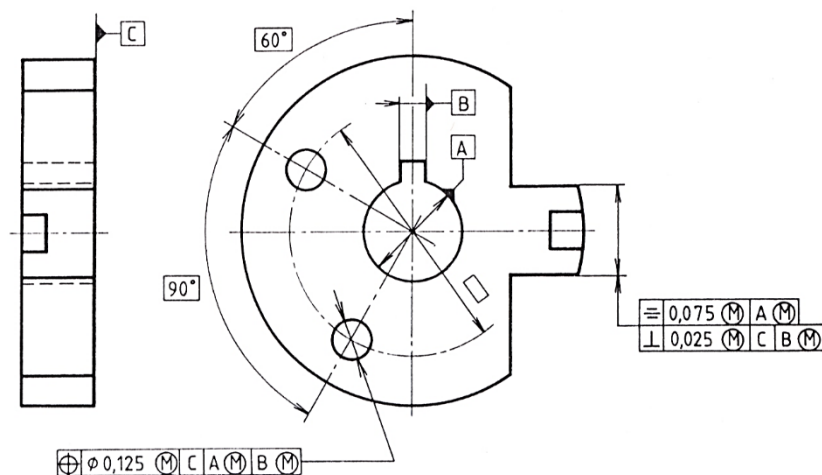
Skutečný tvar - primární A, sekundární B[8]
